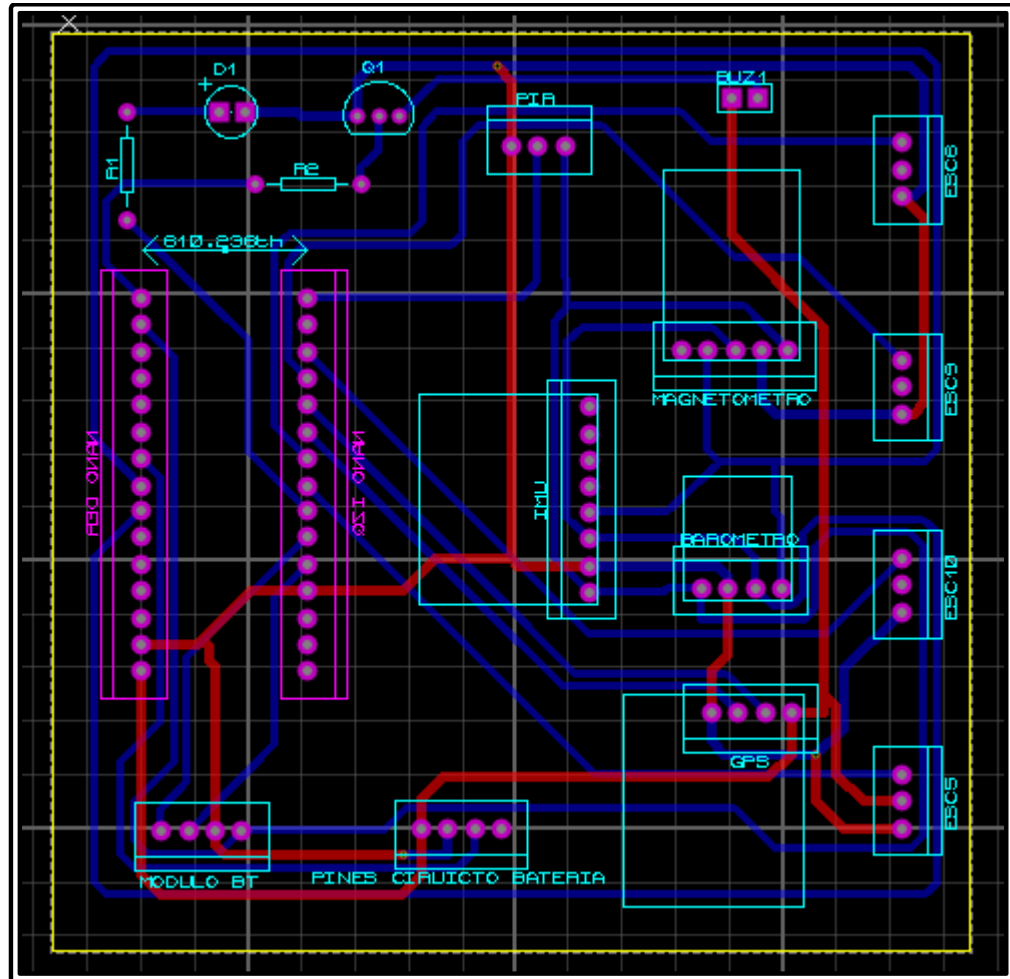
PCB Tarjeta principal del prototipo diseñado en Proteus 8.
